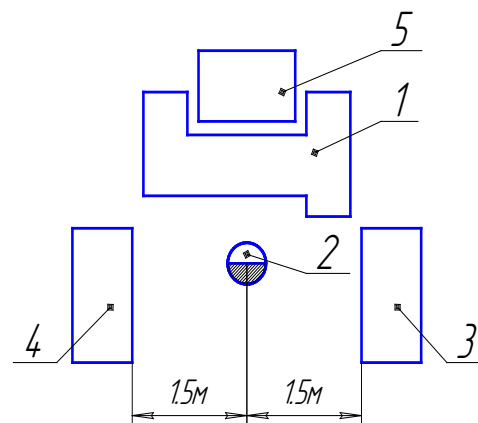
Схема робочого місця верстатника: 1 – верстат; 2 – місце робітника; 3 – стіл для заготовок; 4 – стелаж для деталей; 5 – ящик для відходів.
